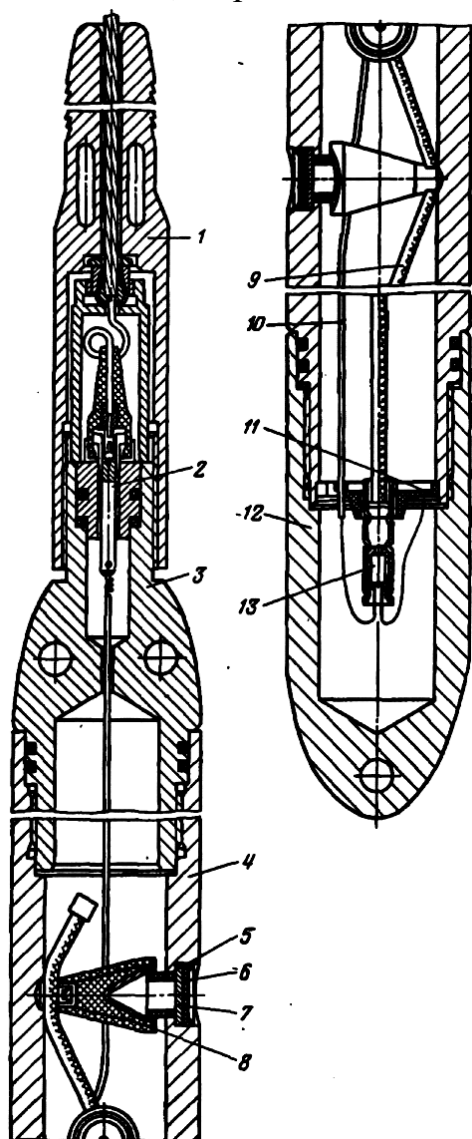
Кумулятивный корпусный перфоратор ПК-103Д многократного использования: 1 – кабельный наконечник; 2 – электроввод; 3 – головка; 4 – корпус; 5 – втулка; 6 – пробка; 7 – опорный диск; 8 – кумулятивный заряд; 9 – детонирующий шнур; 10 – электроввод; 11 – монтажный диск; 12 – наконечник; 13 – взрывной патрон
